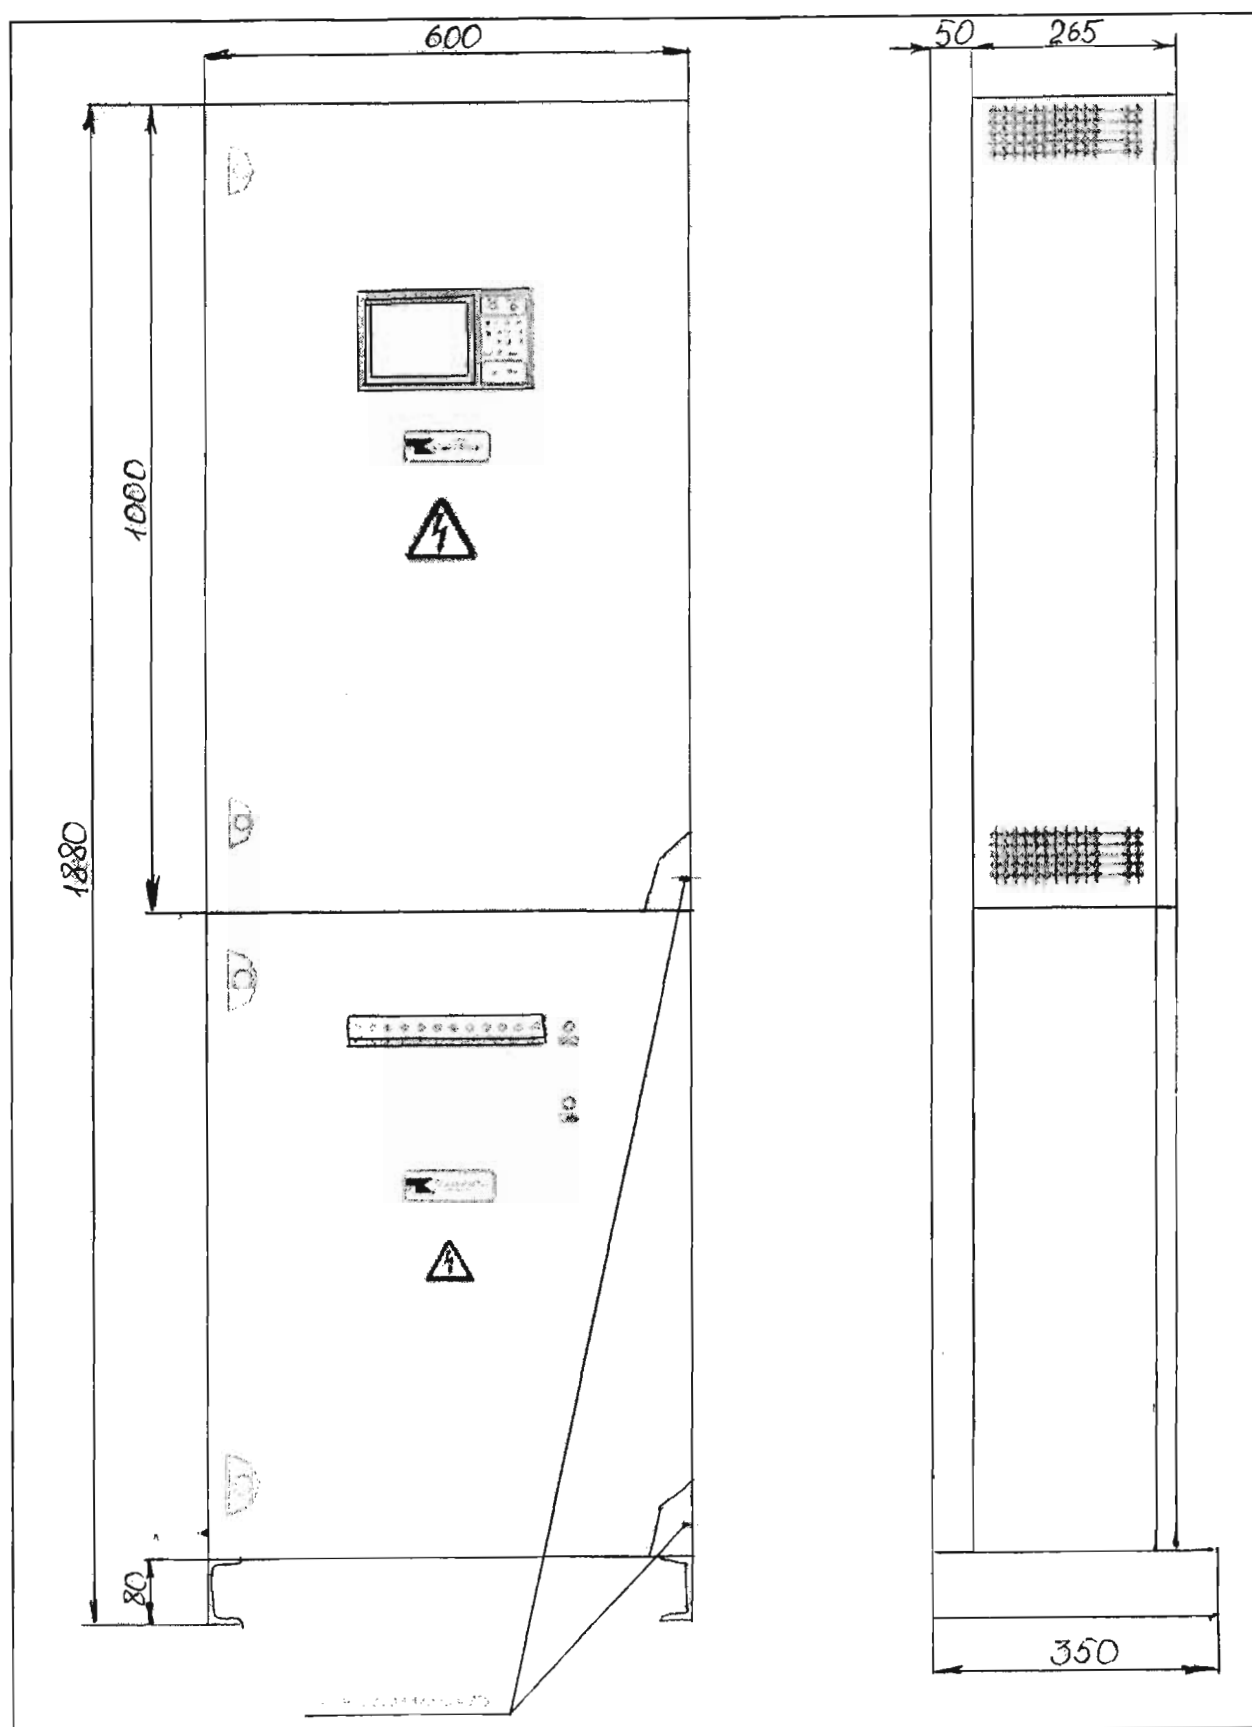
Габаритные, установочные и присоединительные размеры преобразователя АУОТ-М
